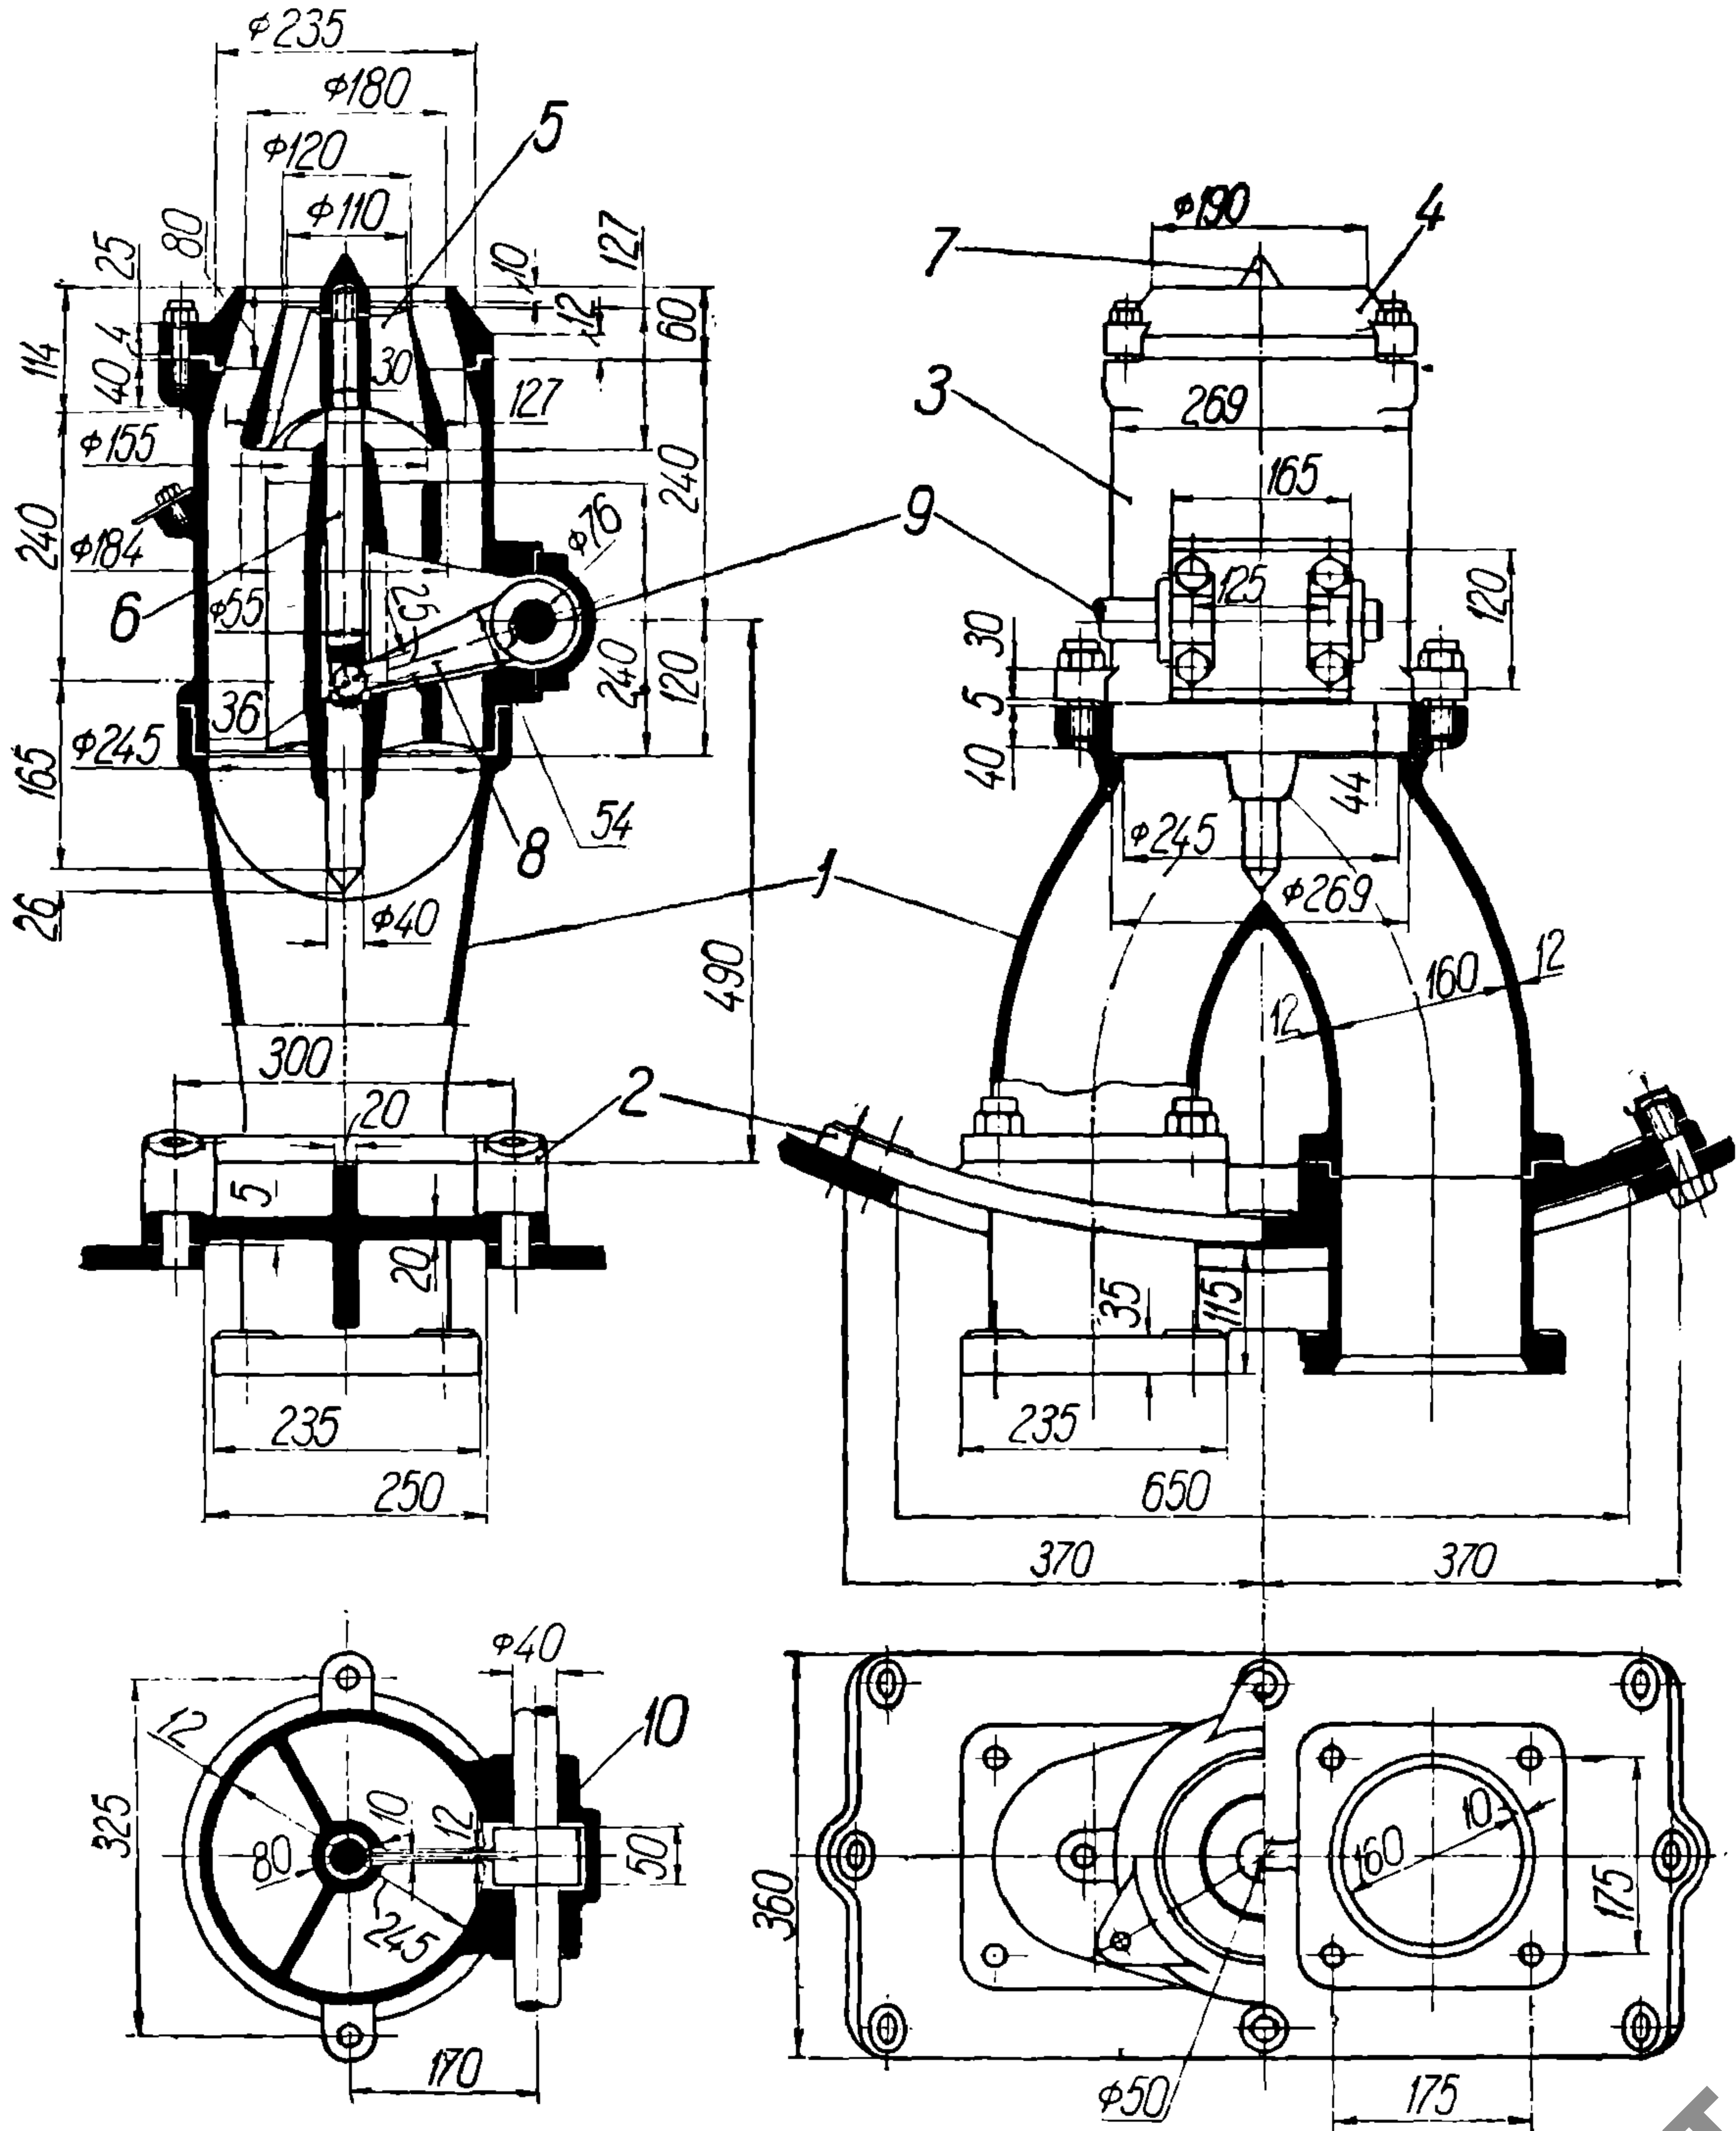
Расположение верхнего конуса в дымовой коробке паровоза 0-4-0 ОД.
